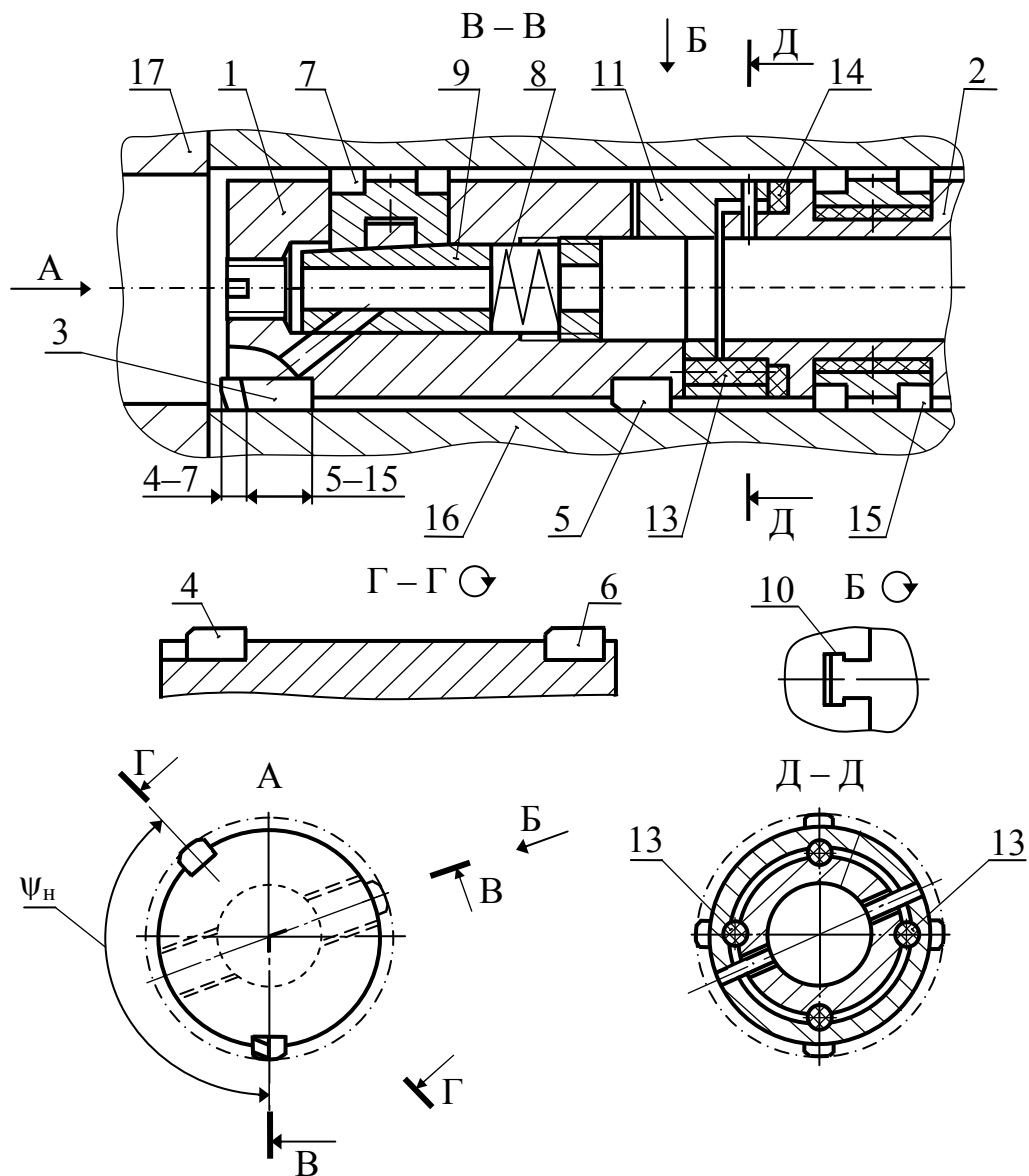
Расточный инструмент с механизмом дискретной подналадки режущего элемента по отверстию кондукторной втулки – калибра.
